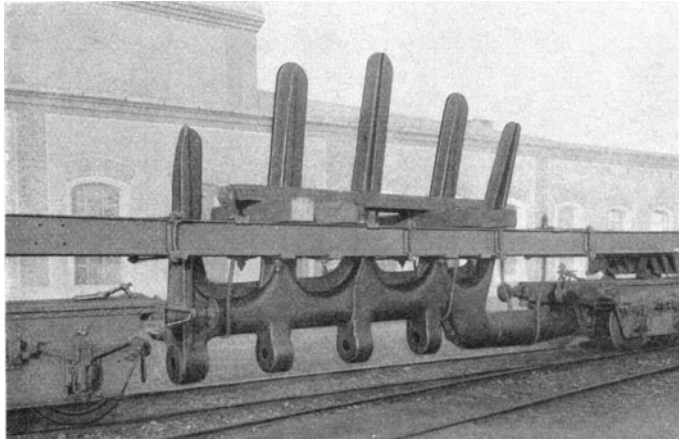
Einteiliger Stahlguß-Ruderrahmen bestehend aus Schaft, Pfosten und 5 Ruderarmen. Gesamtgewicht 21 000 kg.
